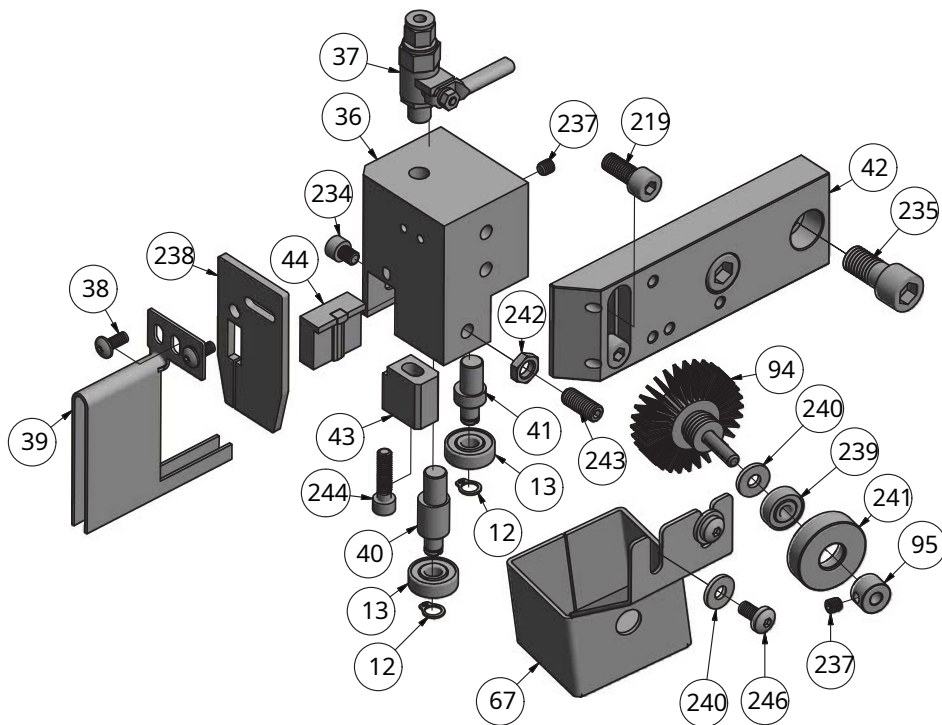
Explosionszeichnung - Dibujo de piezas de repuesto
